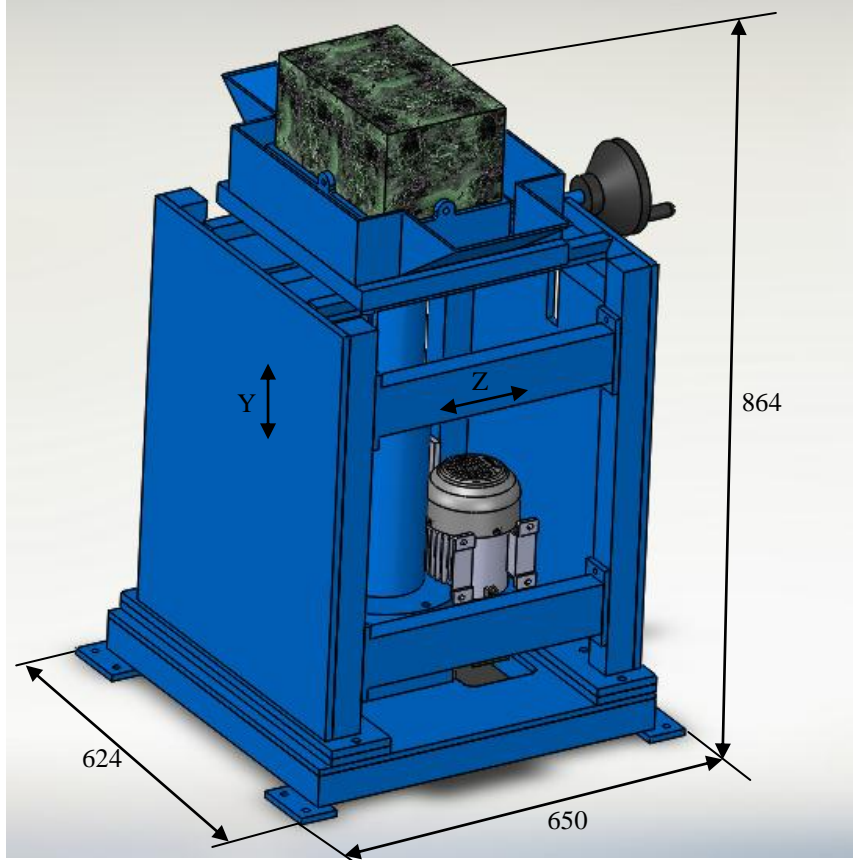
Makinenin kesme mekanizmasının tasarımı (mm).
